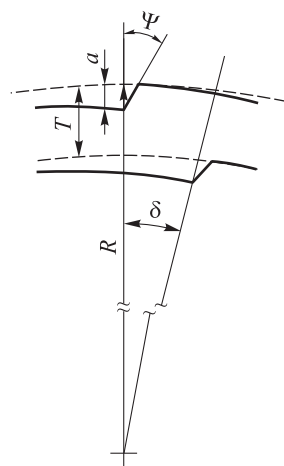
Геометрические размеры поперечного сечения облицовки с наружным и внутренним рифлениями [3]
